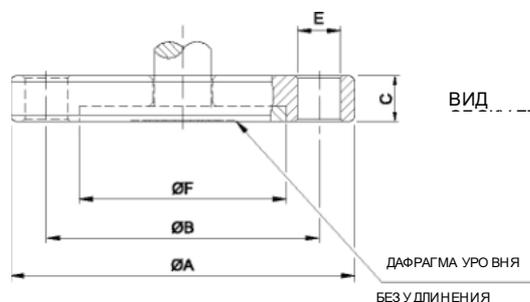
(d) - Размерный чертёж и положения установки для LD290 - Уровневый
